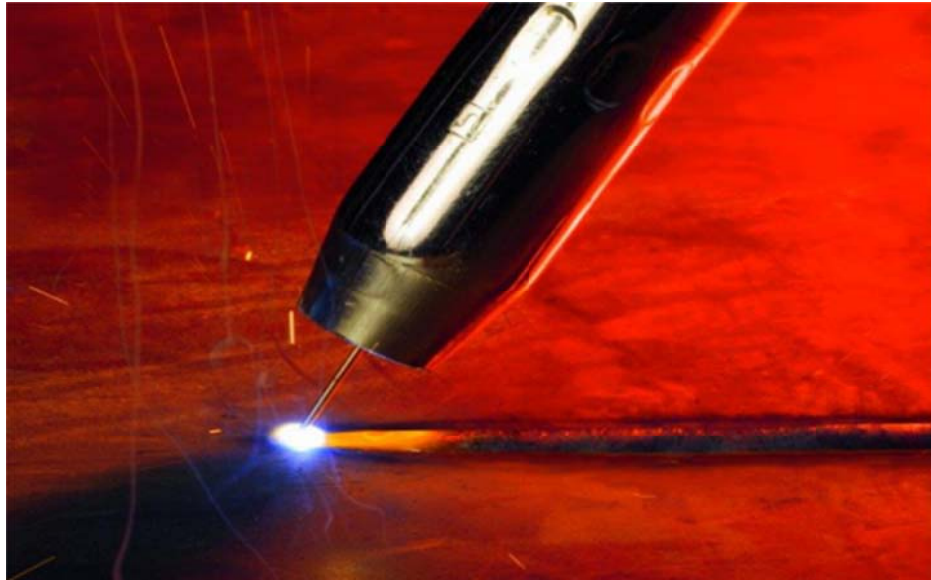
Principe de soudage à l'arc avec électrodes enrobées. [8]
